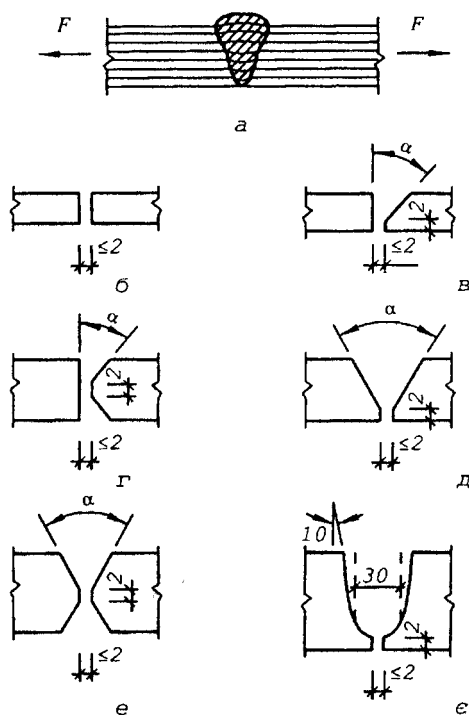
Стикові шви і обробка граней перед зварюванням:
